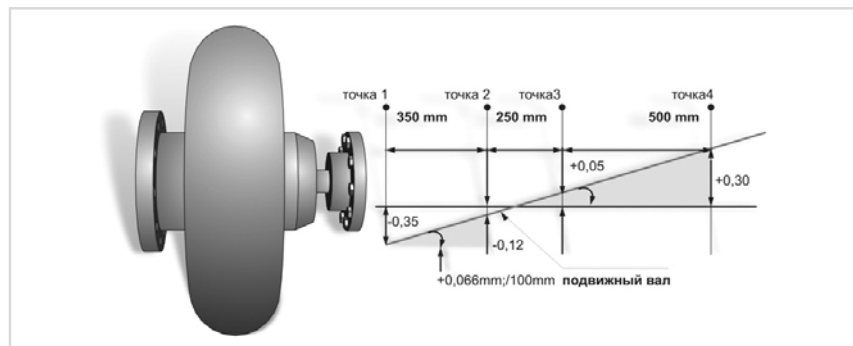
Расчет линии вращения вала привода | We also check laser measuring heads made by Fixturlaser
